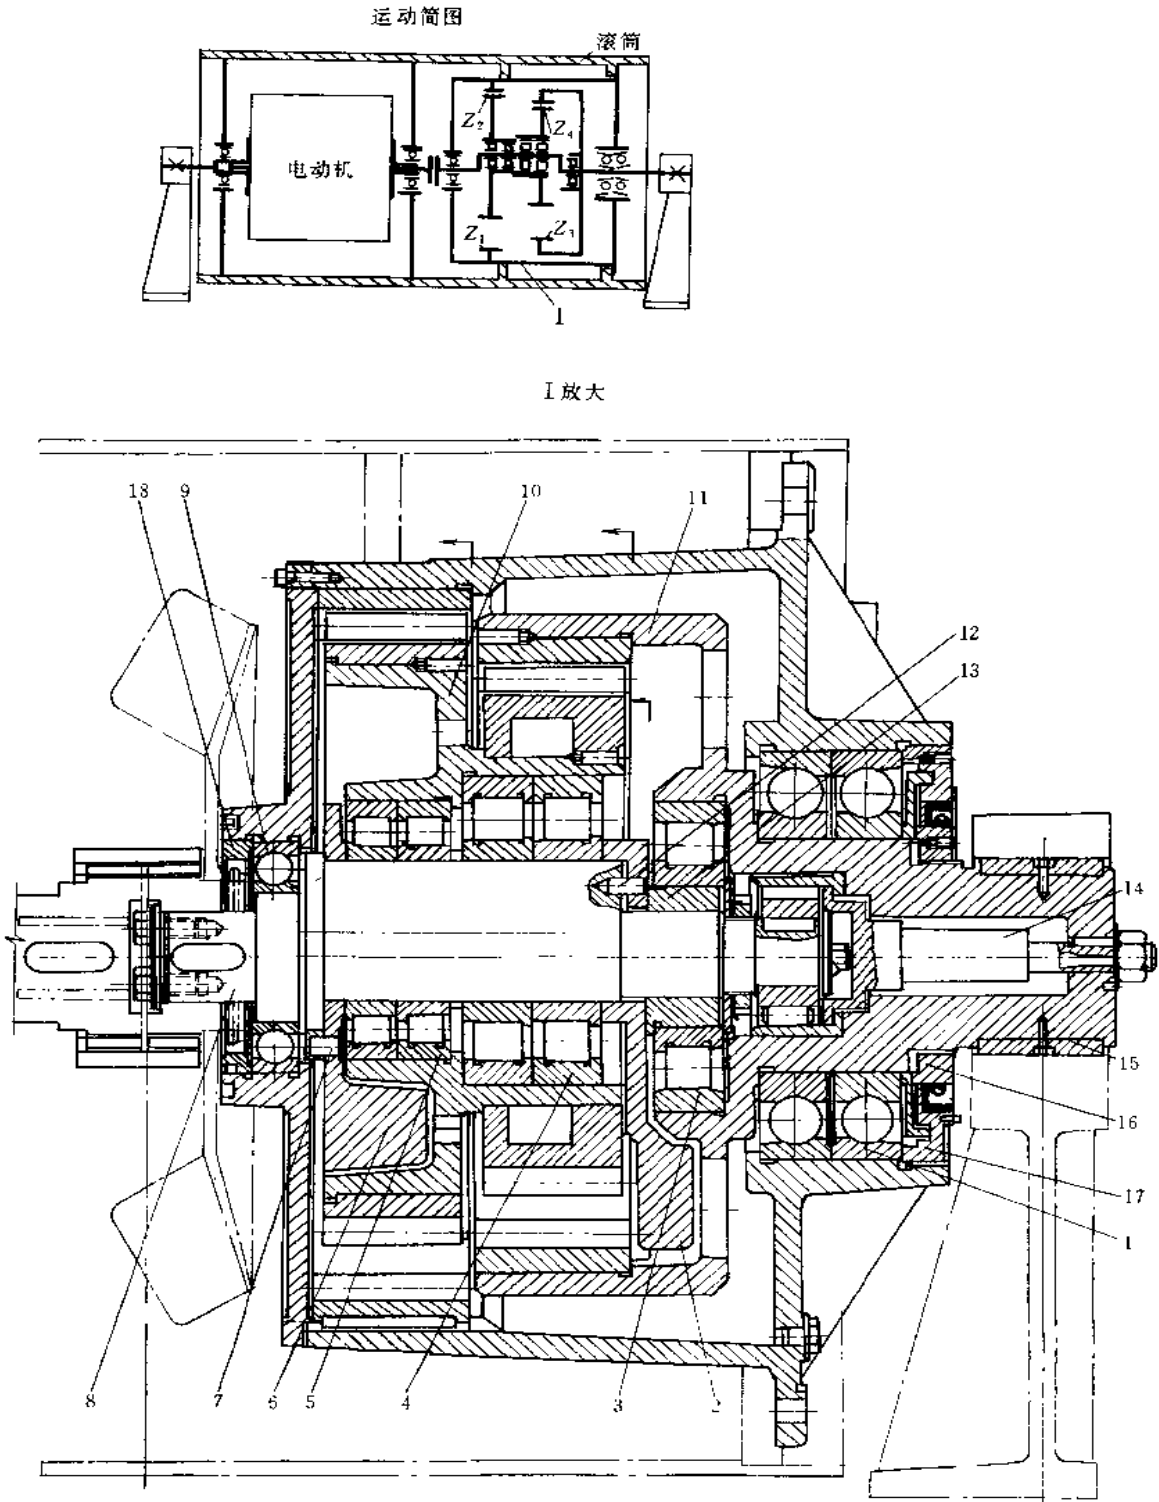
带式输送机滚筒内装式行星齿轮传动支承
